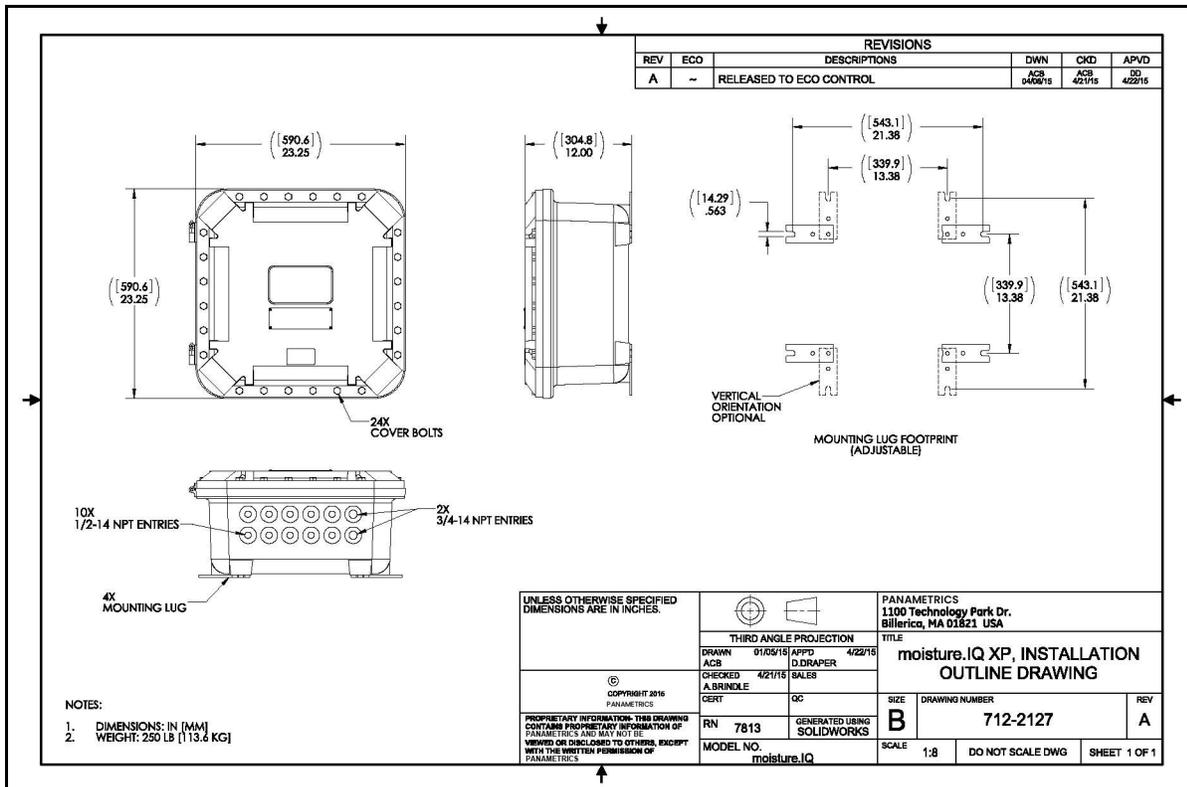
Габаритный чертеж для монтажа XP (чертеж 712-2127_revA, лист 1 из 1)
